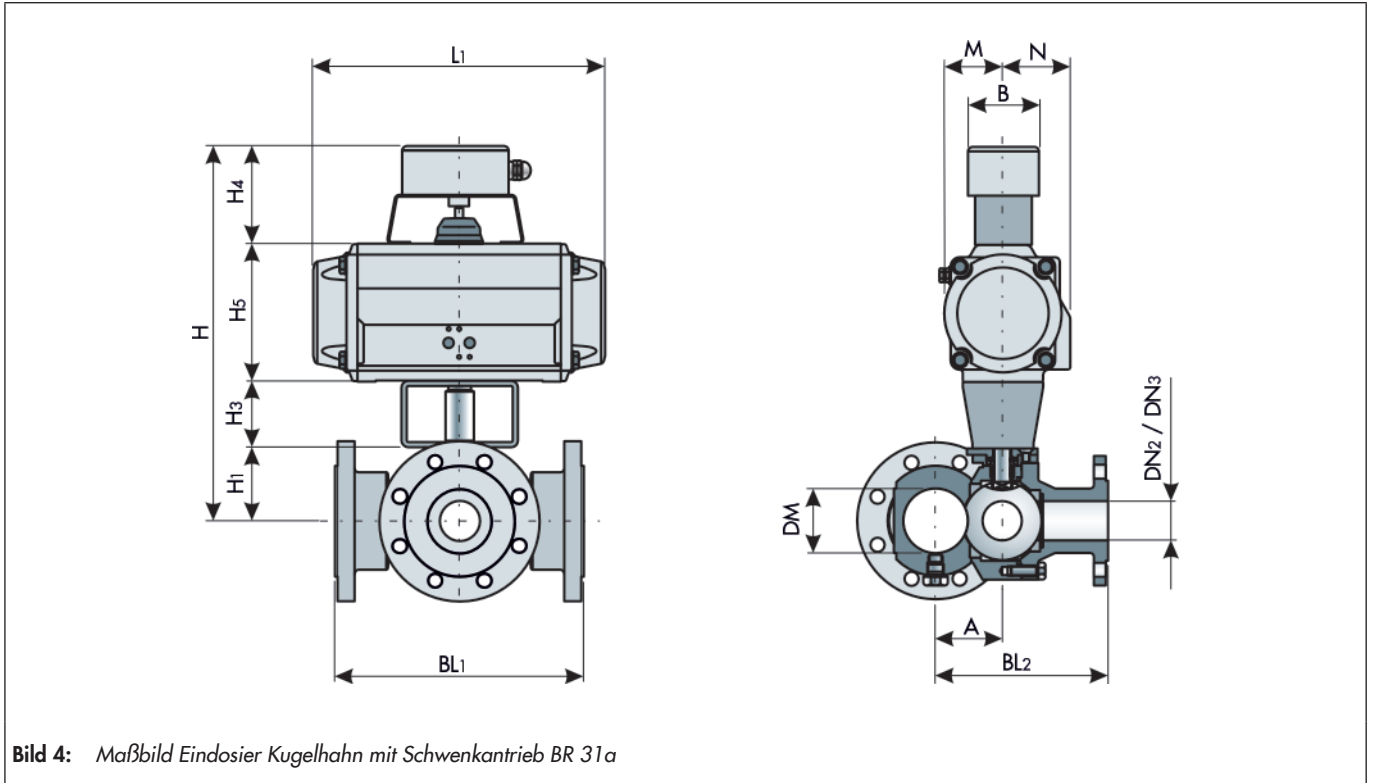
Maßbild Eindsier Kugelhahn mit Schwenkantrieb BR 31a
